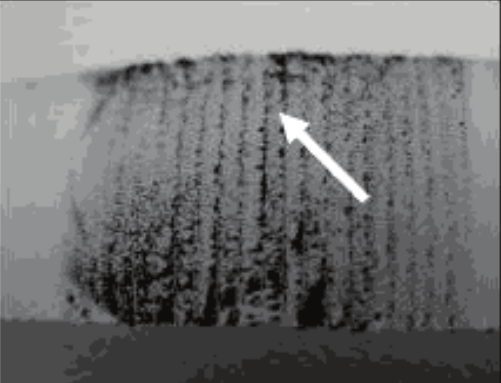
Длина зоны соединения L и примеры дефектов для образцов соединений выполненных муфтовой сваркой с закладными нагревателями (ЗН)
